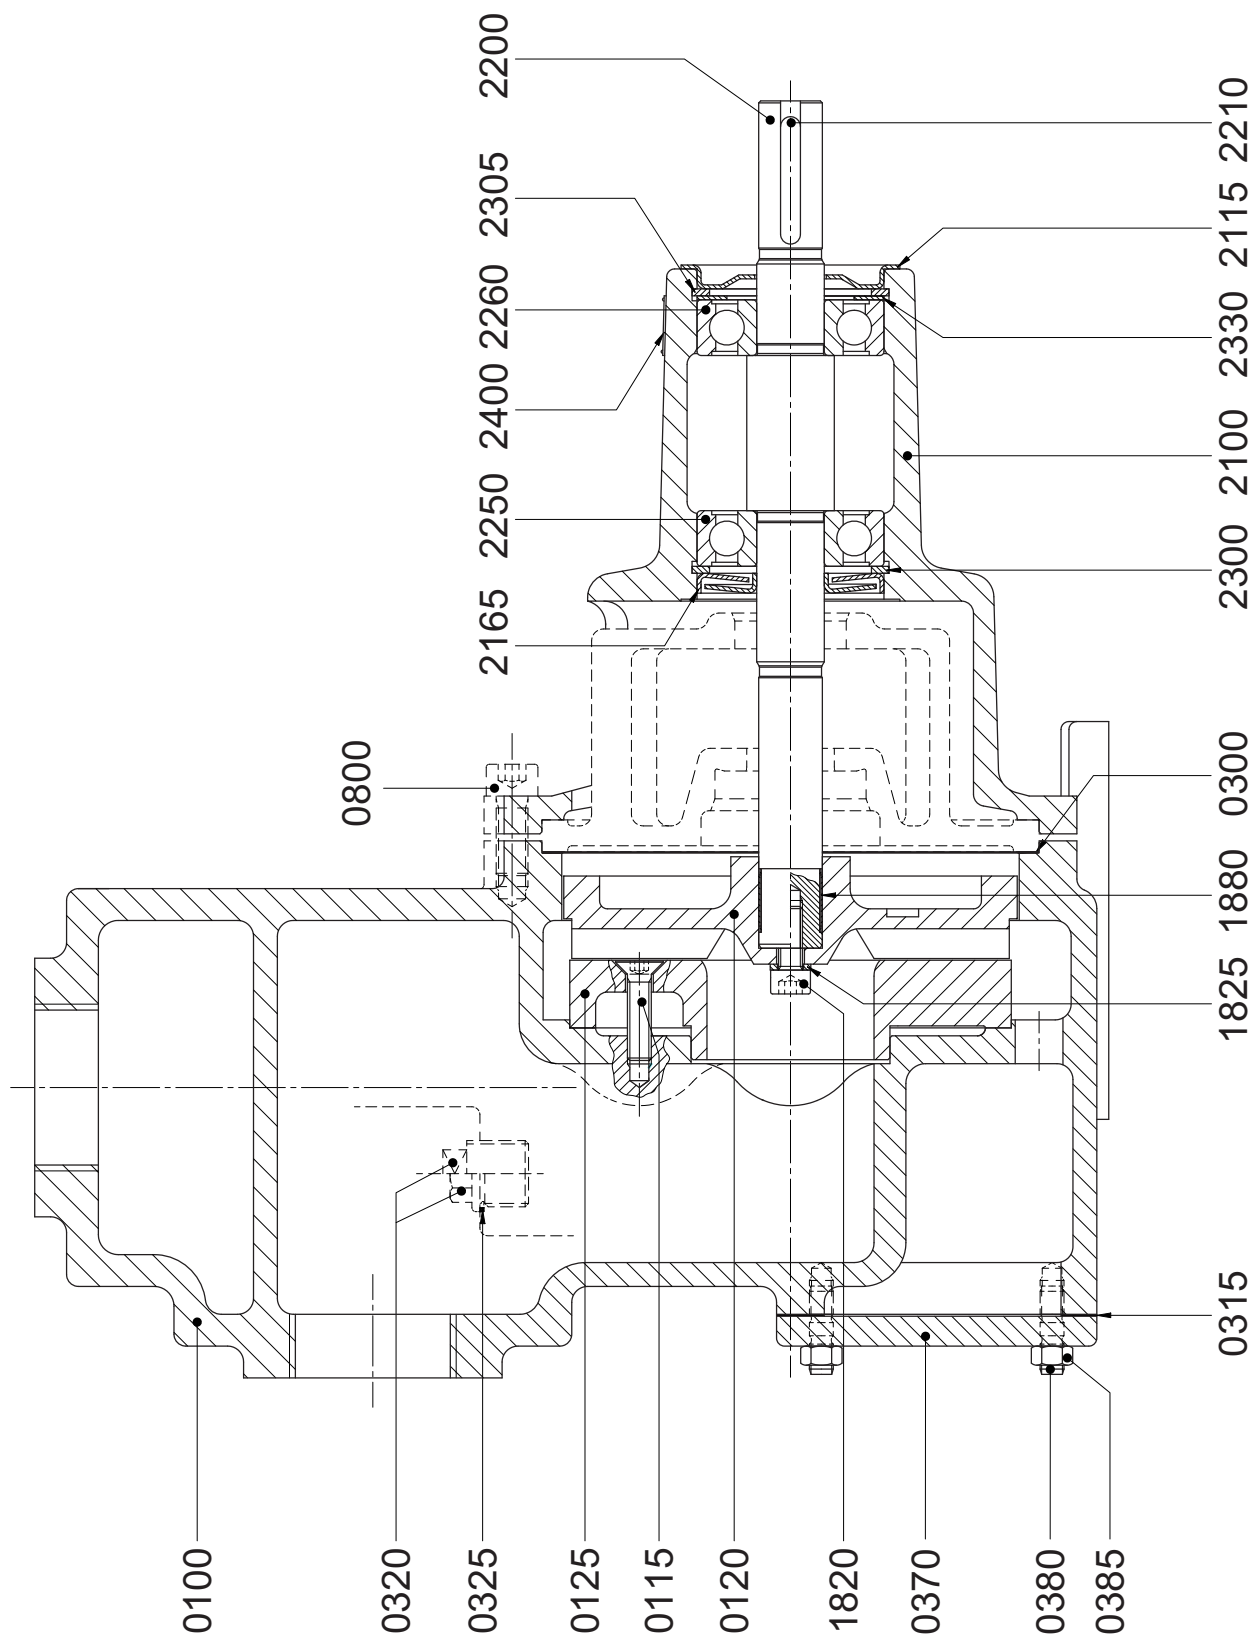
Desenho em corte FRE - grupo de rolamento 1.
